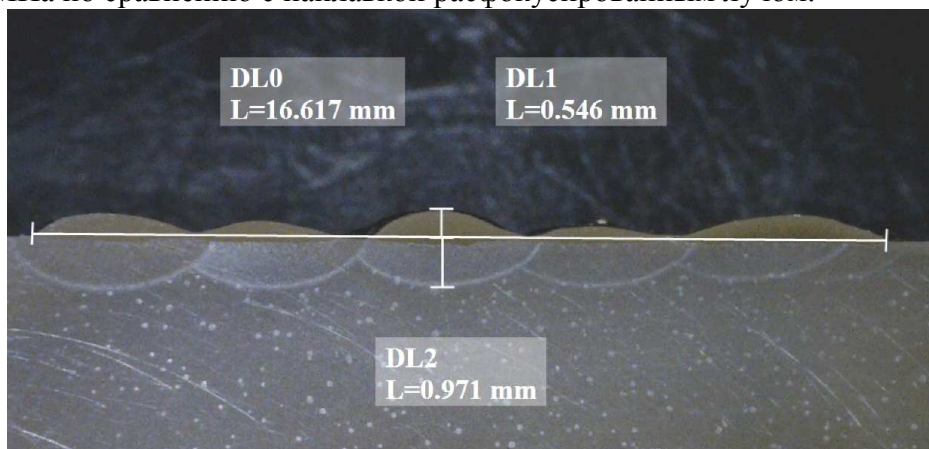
Микрошлиф образца стали 38ХГМ с наплавленными дорожками порошком 20Х13Н2
